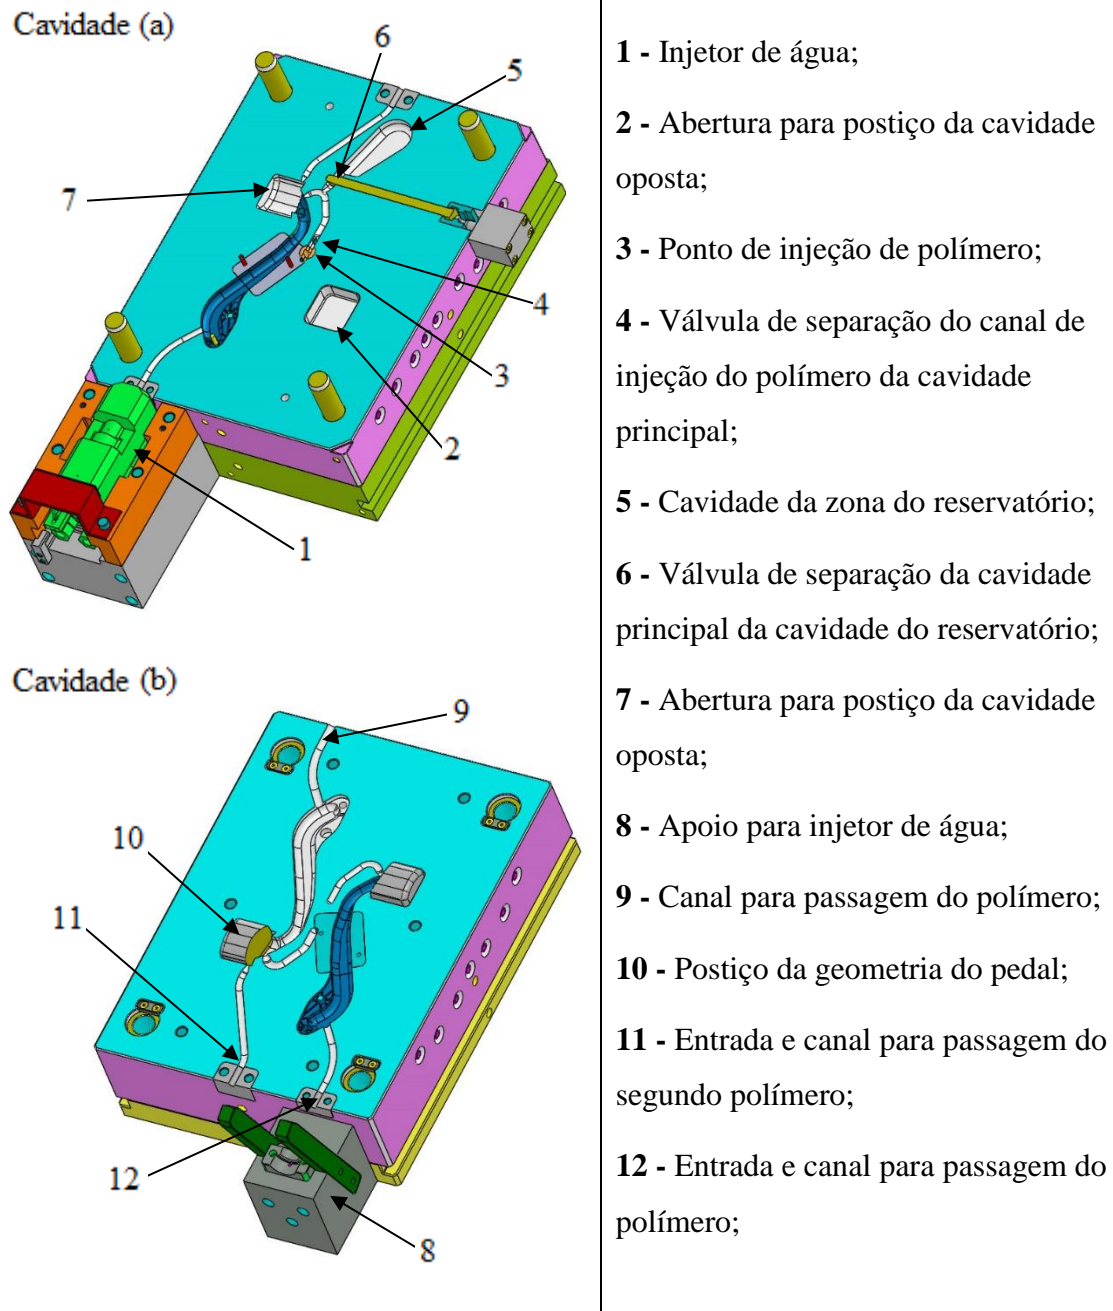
Chapas moldantes do molde protótipo industrial 2
